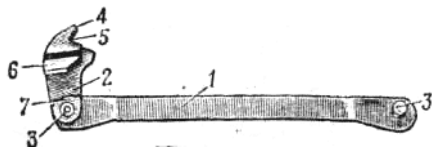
Спусковая тяга с рычагом взвода: 1 – спусковая тяга; 2 – рычаг взвода; 3 – цапфы спусковой тяги; 4 – разобщающий выступ рычага взвода; 5 – вырез; 6 – выступ самовзвода; 7 – пяточка рычага взвода
